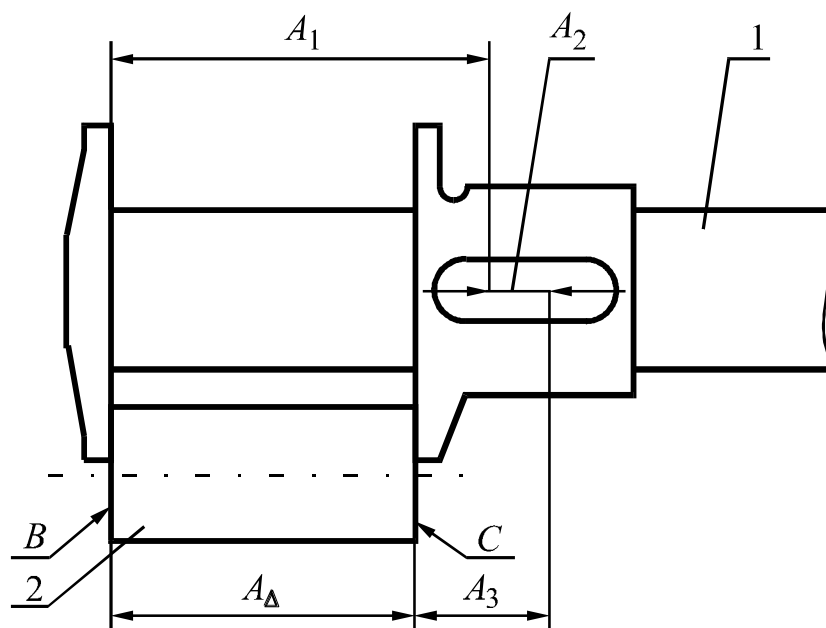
Схема измерительной размерной цепи: 1 – измерительный инструмент; 2 – деталь (B и C – действительные поверхности детали)
